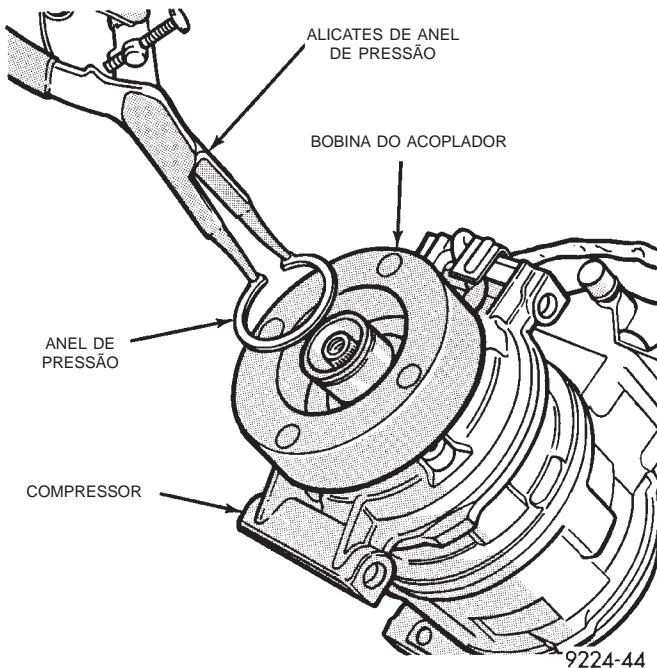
Remoção/Instalação do Anel de Pressão da Bobina do Acoplador
